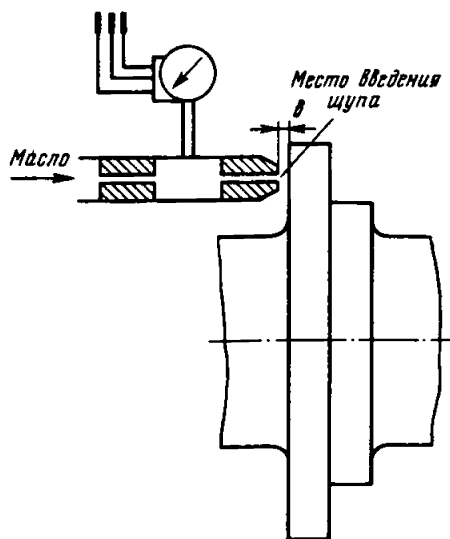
Схема гидравлической защиты от осевого сдвига ротора
